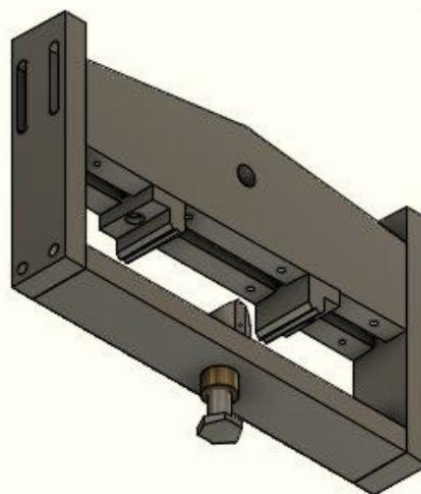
Dispositivo adaptado a torno universal. (esquema extraído de patente [2])
